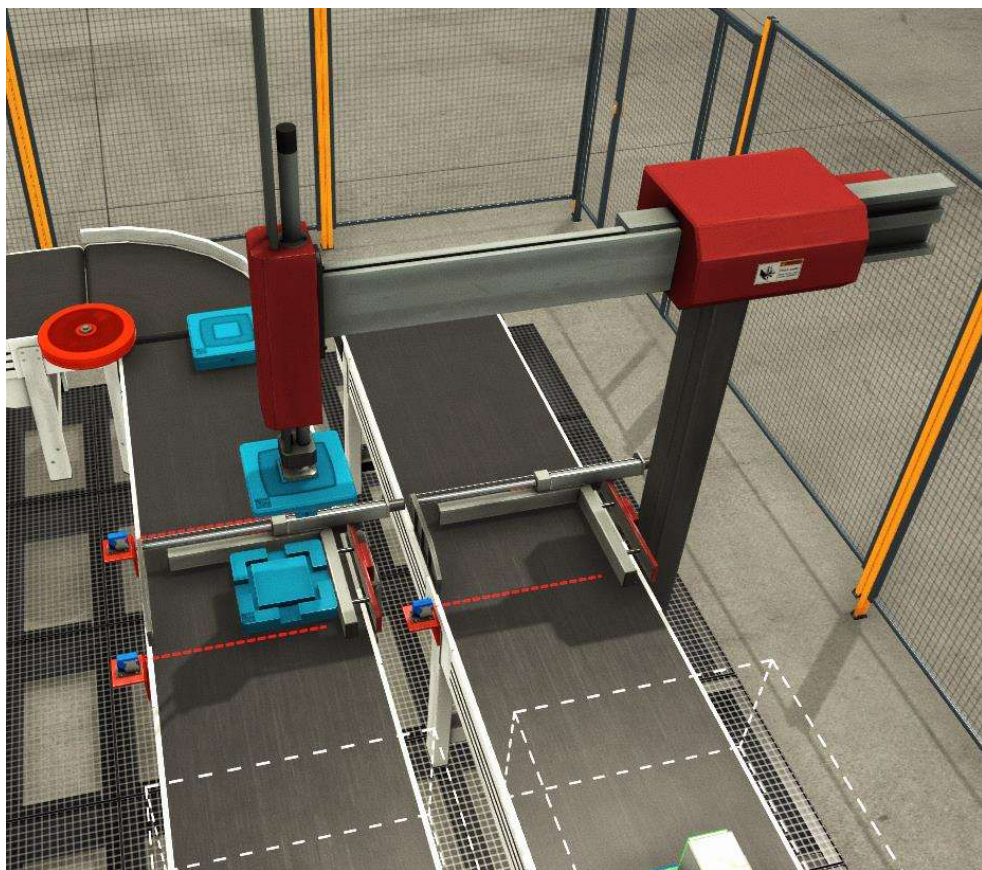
Stanowisko montażowe w wizualizacji Factory I/O
